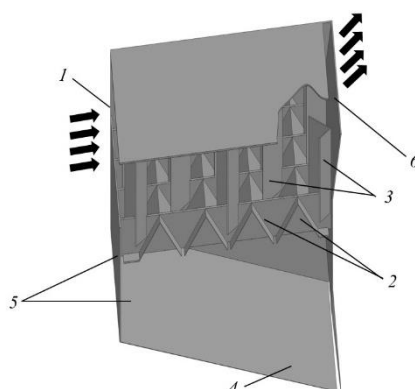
Трехмерное изображение нового очистительного устройства с прямоугольными пластинами: 1 – входной патрубок; 2 – сепарационная решетка; 3 – прямоугольные пластины; 4 – бункер для сбора частиц; 5 – корпус устройства; 6 – выходной патрубок.
